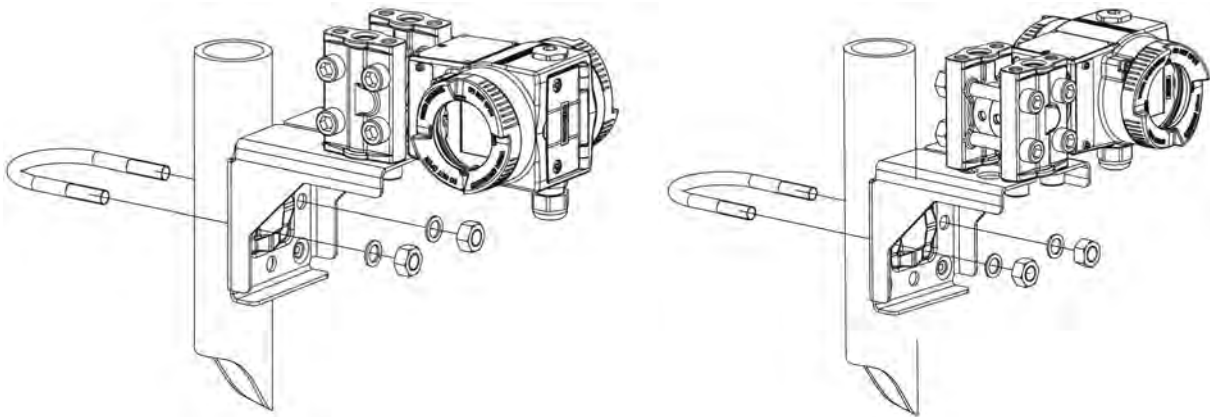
Befestigung des Druckmessumformers mit Montagewinkel für senkrechte Wirkdruckleitungen
